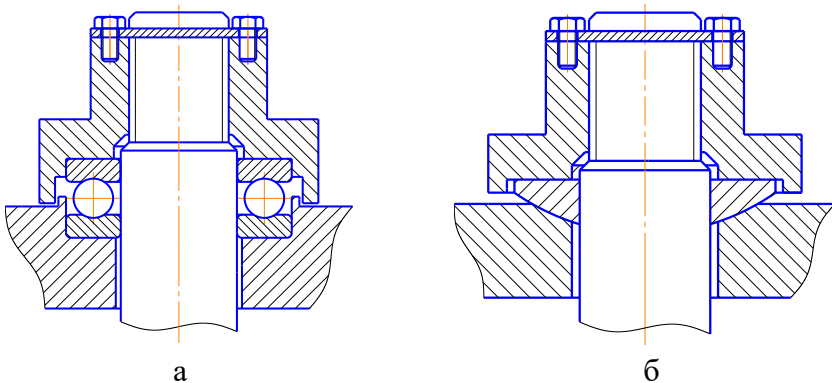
Установка крюка: а – на упорном подшипнике;
